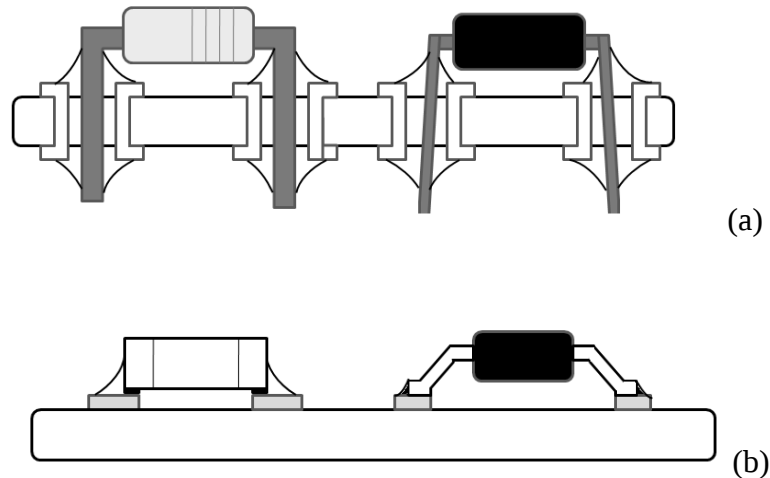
Esquemático de tecnologías en un PCB: (a) Componentes de la tecnología THT atravesando un PCB, (b) Componentes de la tecnología SMT montado sobre un PCB [2].
